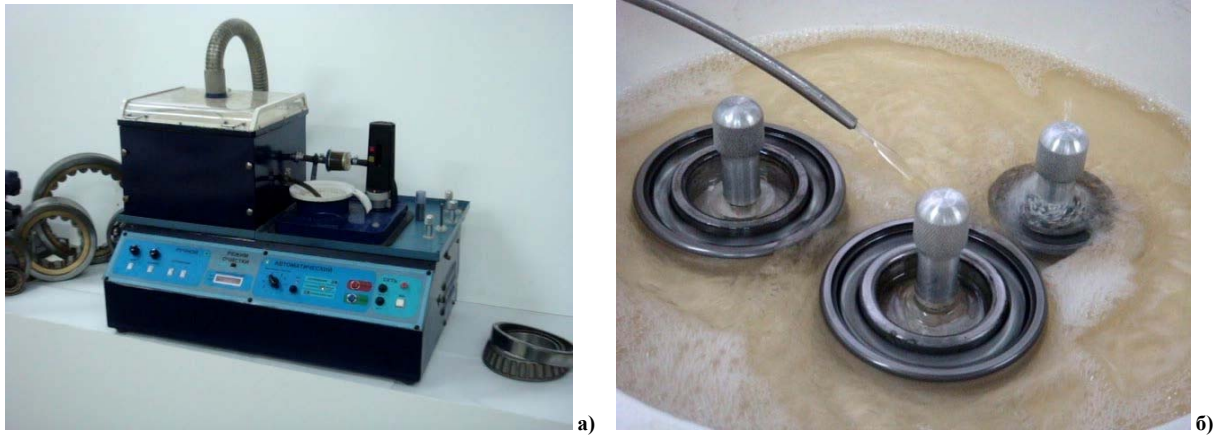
Внешний вид стенда очистки шарикоподшипников ОПШ-01 (а) и камера очистки трех подшипников с разными типоразмерами (б)
